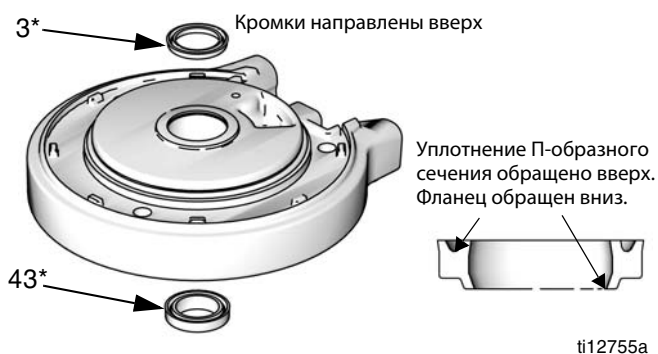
Установка уплотнения П-образного сечения пневматического двигателя
